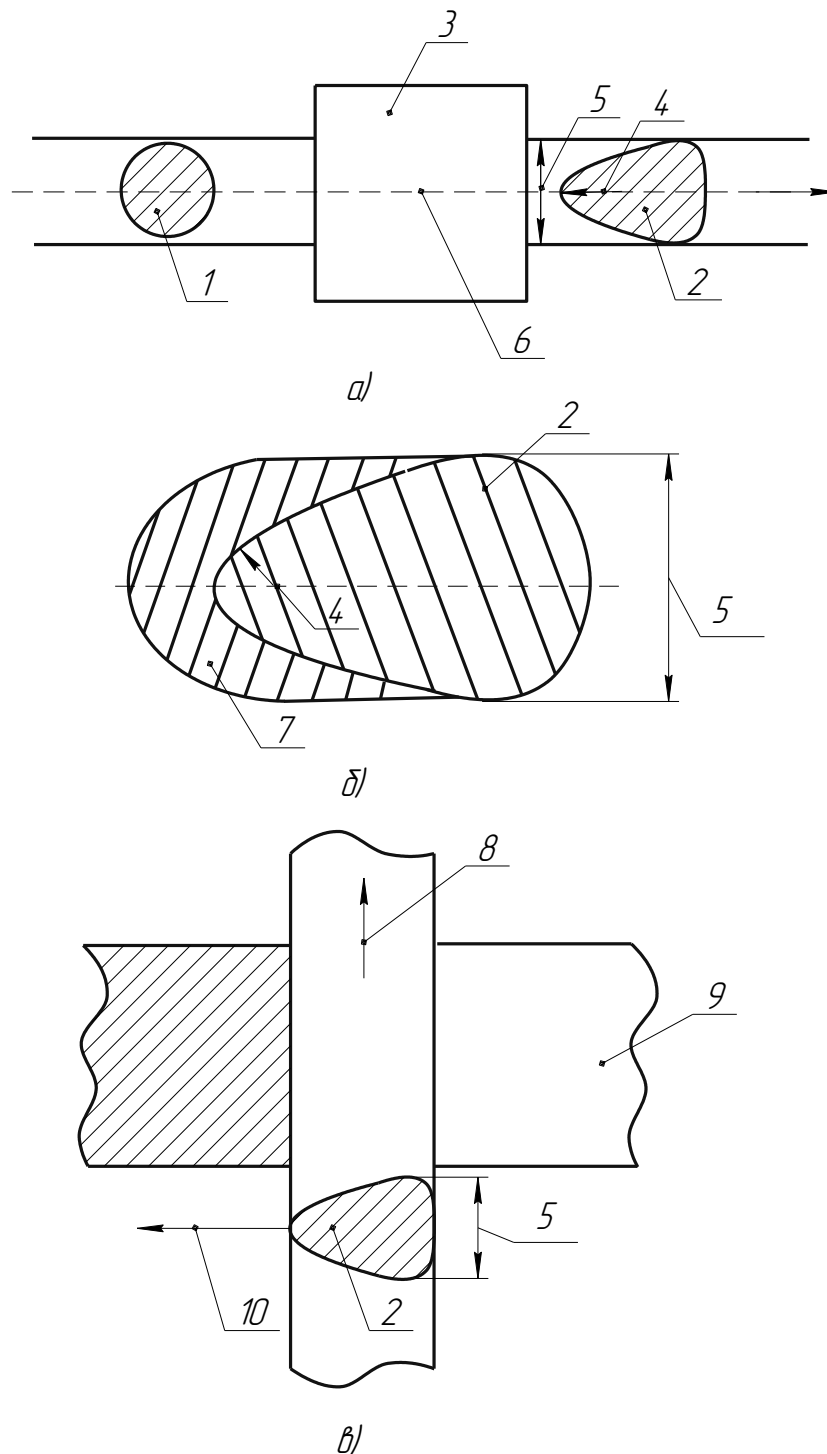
Способ и инструмент для эрозионно-термической обработки
